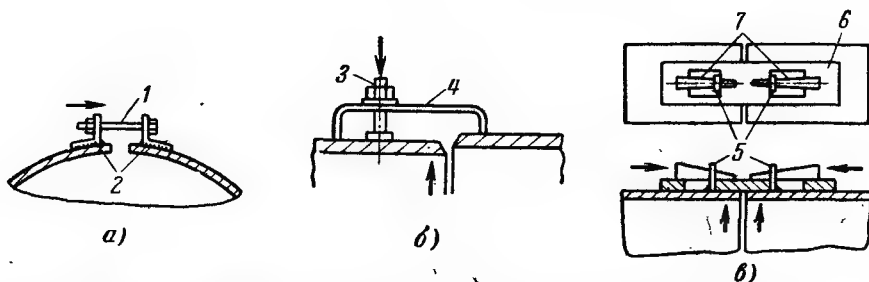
Натяжные приспособления для сборки обечайки под сварку.
